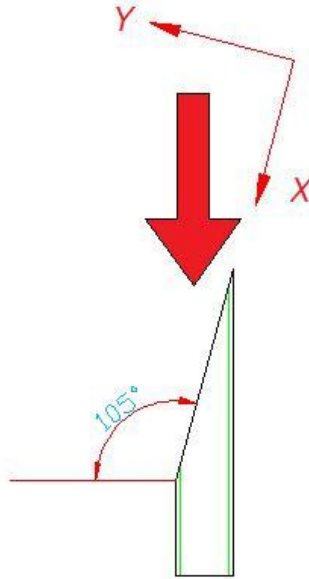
Esquema de fuerzas en el cordón de soldadura del soporte del ventilador
